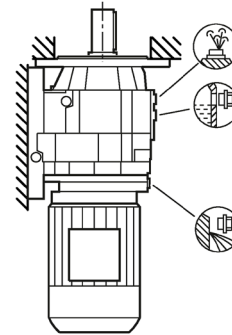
Einbaulagen für Stirnradgetriebe DB/ZB Fuß- / Flanschausführung Baugröße 29
